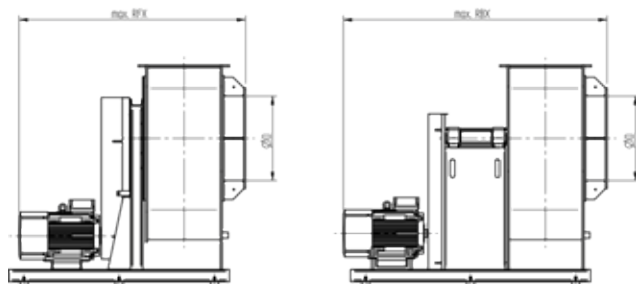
| Vue d'ensemble des ventilateurs HF R | entraînement par courroie:
